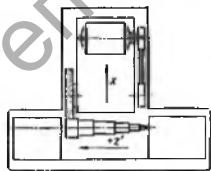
Система координат круглошлифовального станка с ЧПУ
